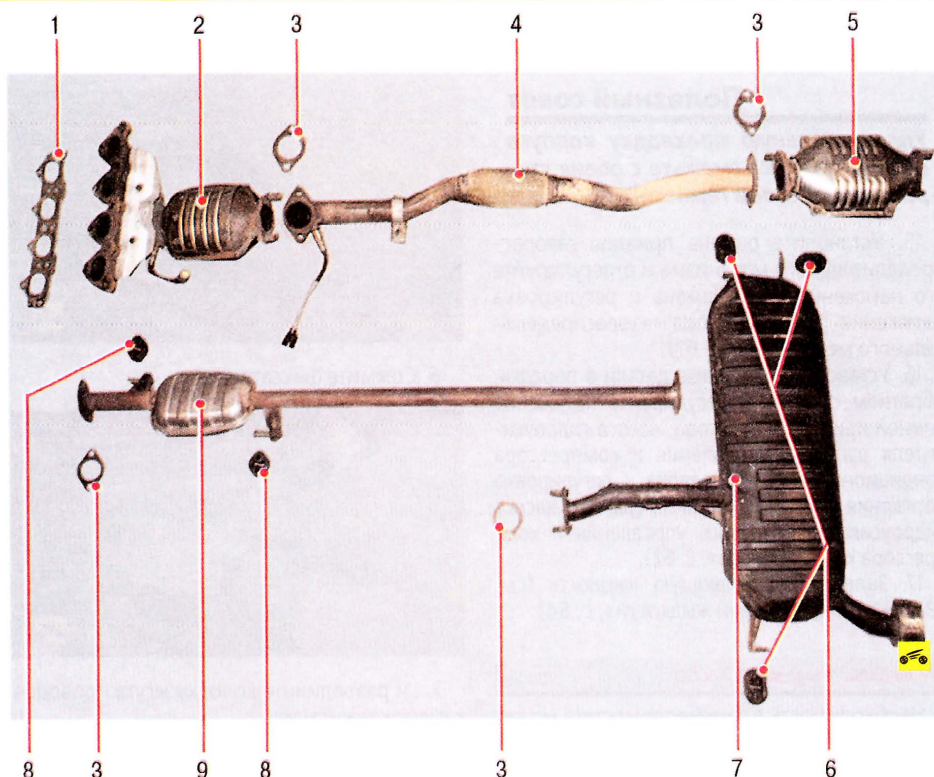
Узлы системы выпуска отработавших газов: 1 – уплотнительная прокладка катколлектора; 2 – катколлектор; 3 – уплотнительная прокладка фланца трубы системы выпуска; 4 – приемная труба; 5 – дополнительный нейтрализатор; 6 – подушки подвески основного глушителя; 7 – основной глушитель; 8 – подушка подвески труб системы выпуска; 9 – дополнительный глушитель
